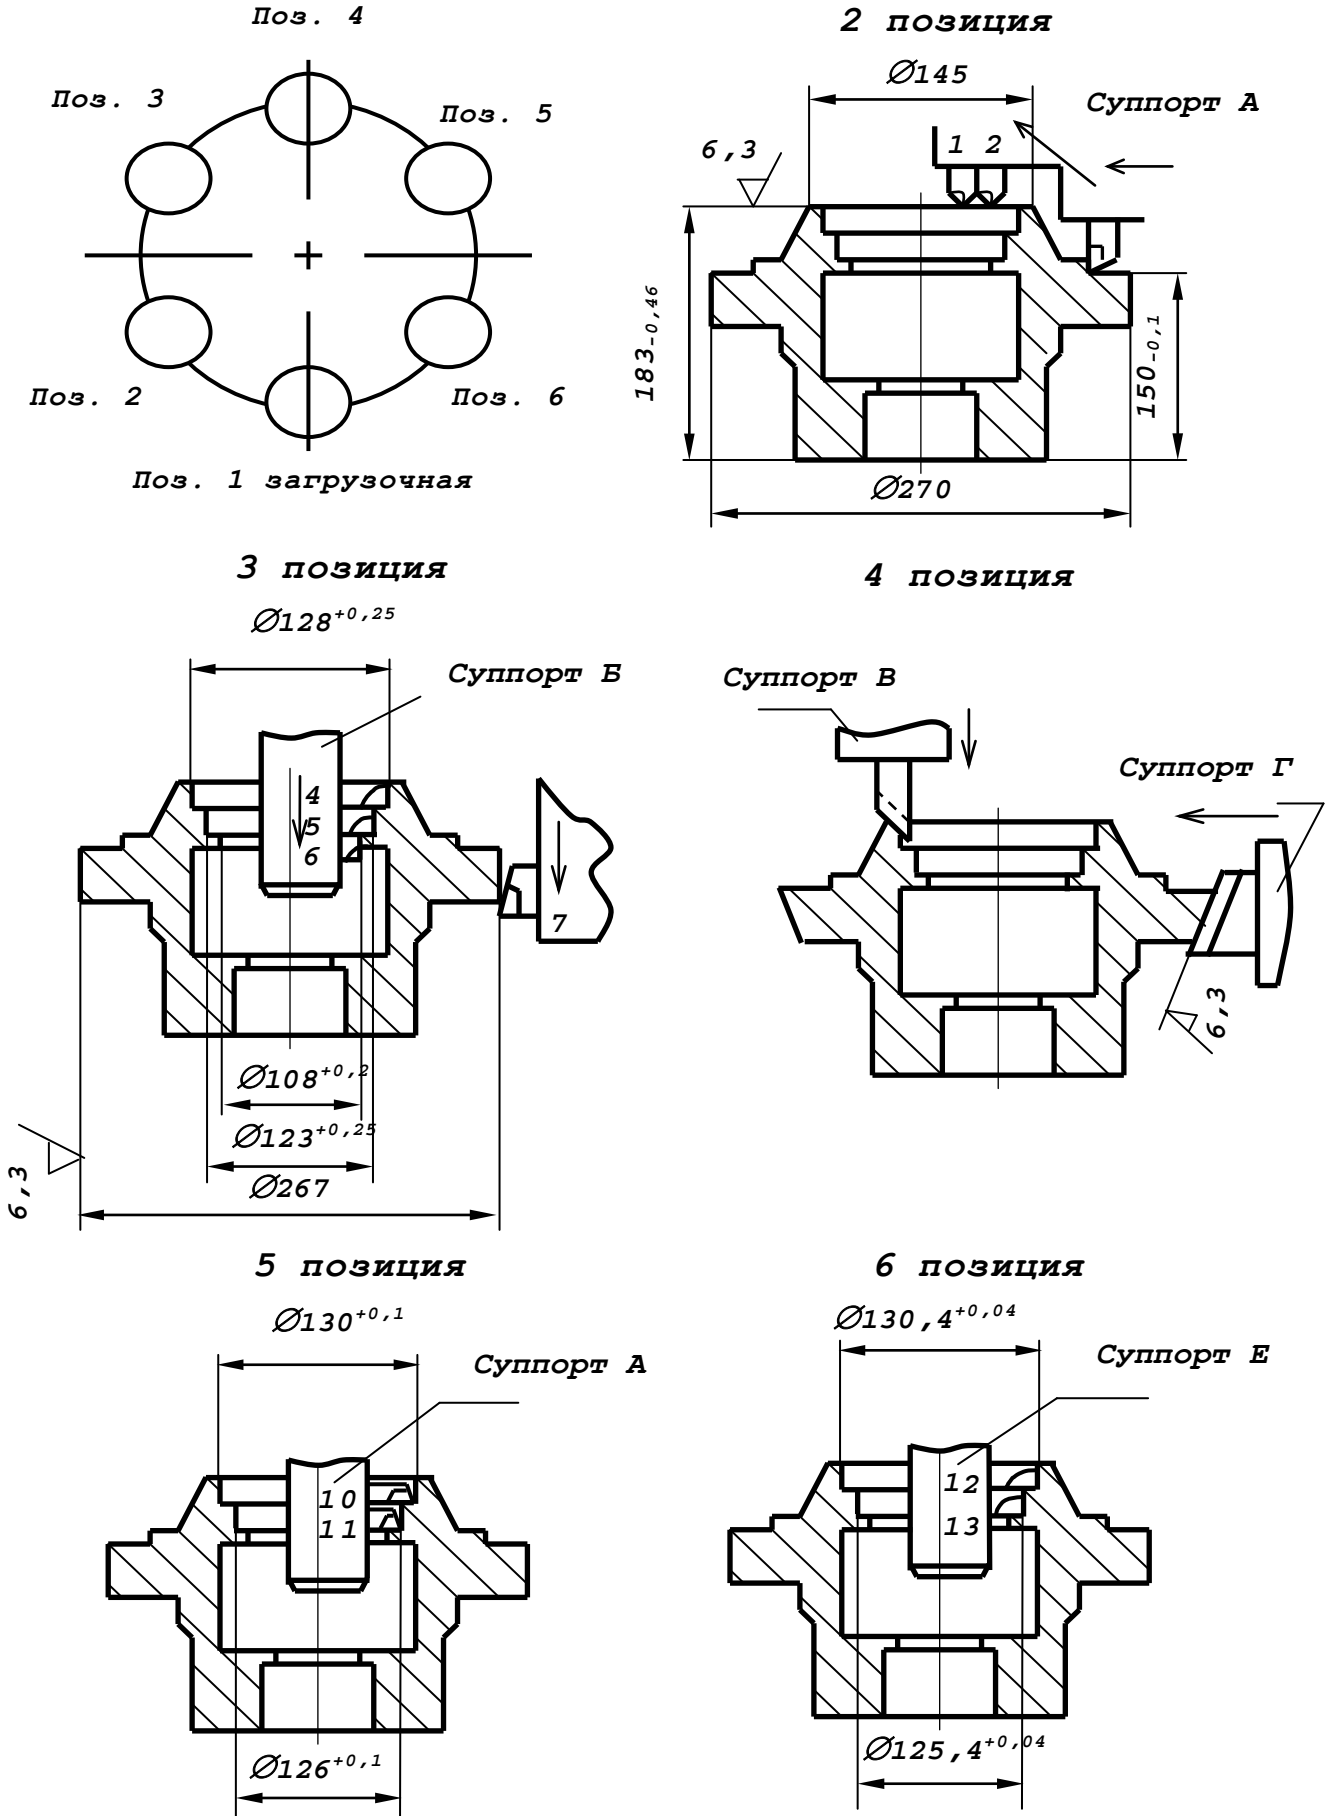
Эскиз обработки и схема расположения позиций на токарном полуавтомате
